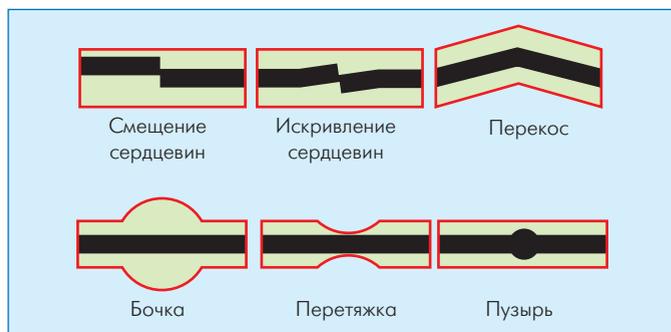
Примерный вид дефектов сварных соединений волокон на экране автоматизированного сварочного аппарата
